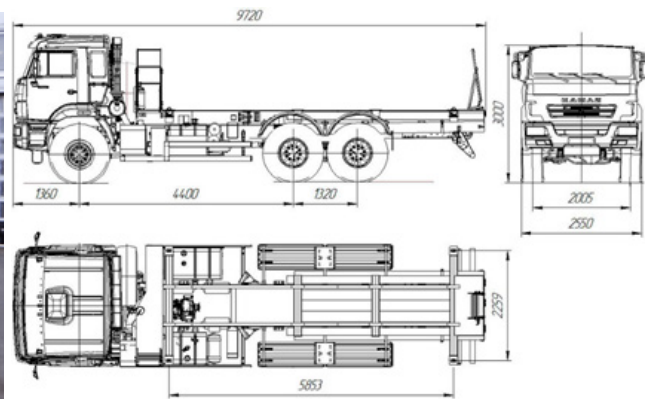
Габаритные размеры шасси КамАЗ-43118
